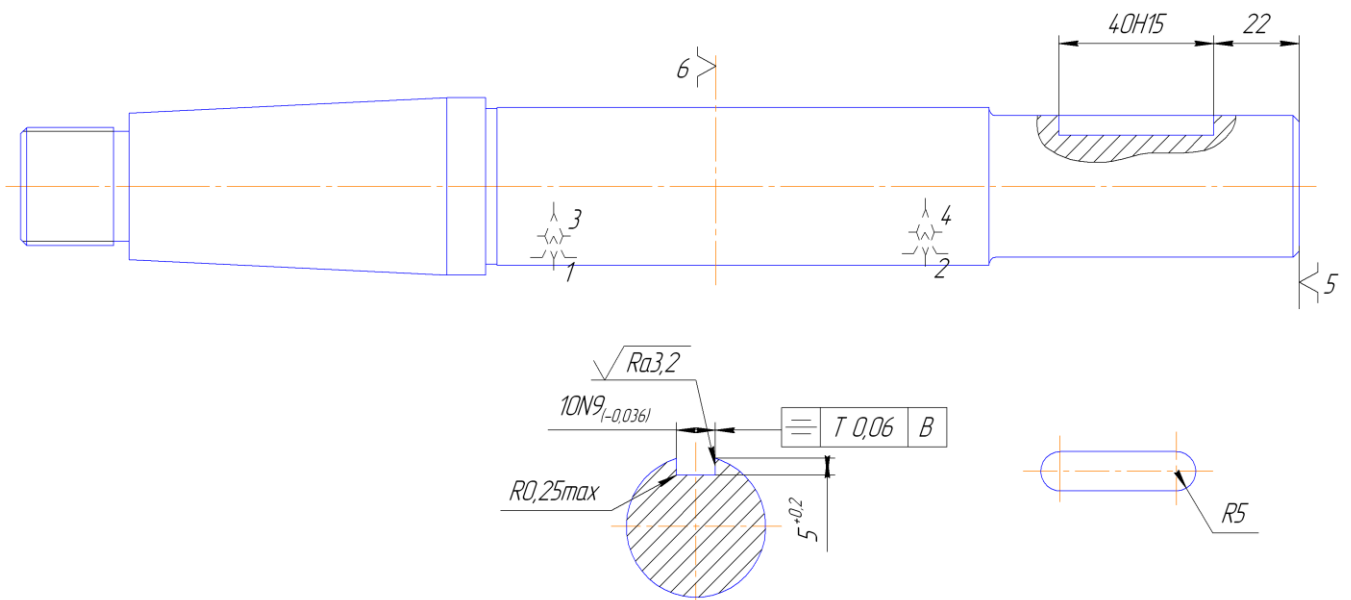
Ескіз на фрезерування паза 10N9_(-0,036) в валі РЦ 001.07.12
